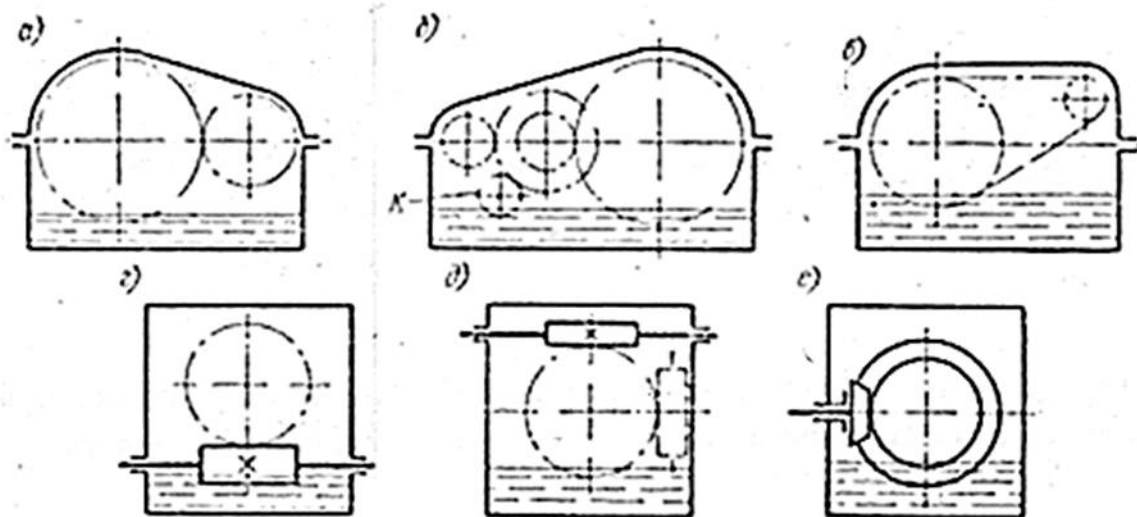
Смазывание погружением (картерное смазывание): а — цилиндрическая зубчатая передача; б — цилиндрическая зубчатая передача со вспомогательным смазывающим колесом; в — цепная передача; г, д — червячная передача; е — коническая зубчатая передача
